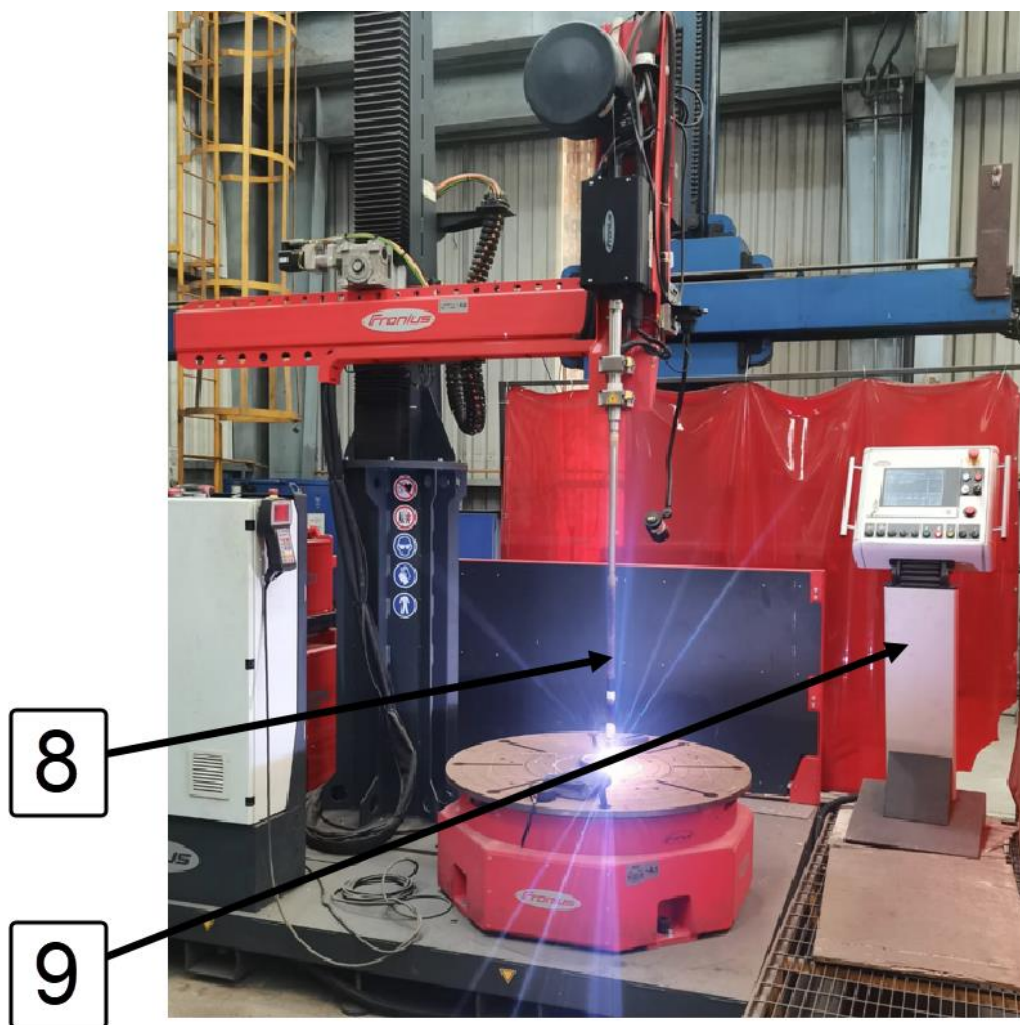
Foto do equipamento de revestimento de soldagem mecanizado CCC (compact cladding cell). Angulo 2.
